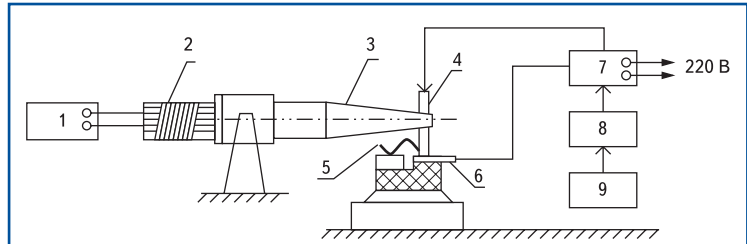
Схема УЗ-микросварки с токовой активацией: 1 — генератор УЗ-колебаний; 2 — акустический трансформатор; 3 — волновод; 4 — сварочный капилляр; 5 — алюминиевая проволока; 6 — контактная площадка; 7 — блок токовой активации; 8 — блок питания; 9 — блок управления
